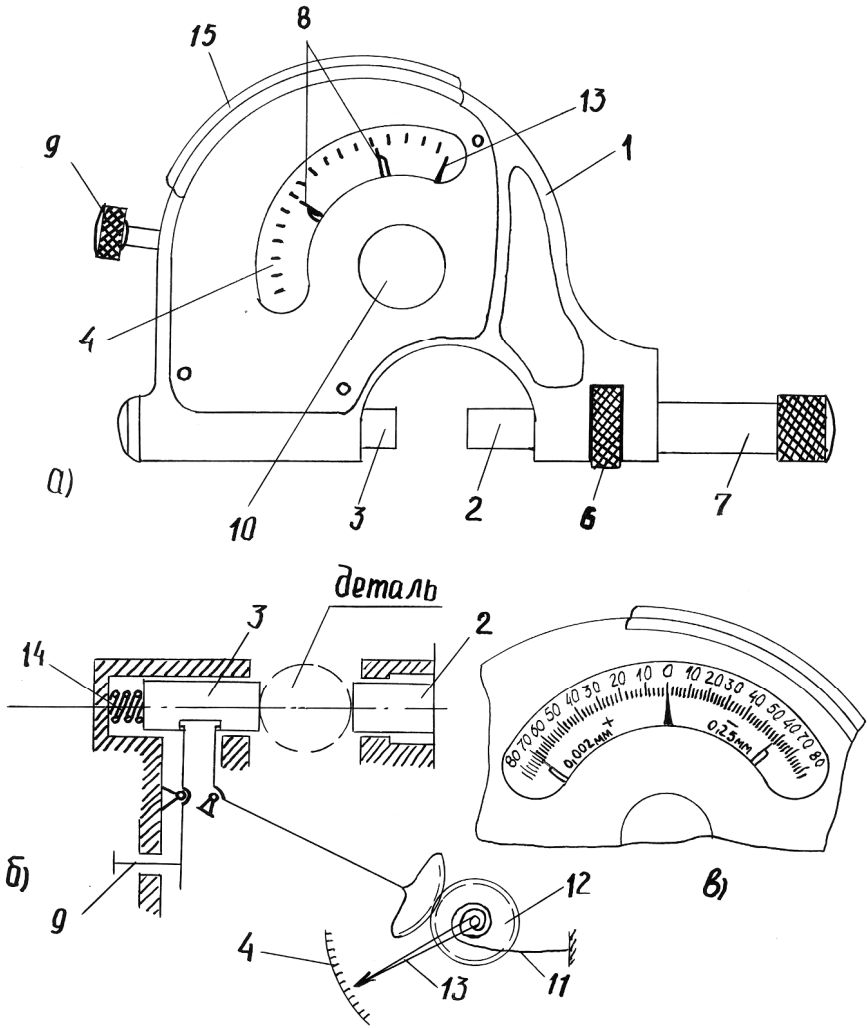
Важільна скоба: *а* – загальний вигляд; *б* – важільно-зубчастий механізм; *в* – шкала; 1 – корпус; 2 – переставна п'ятка; 3 – рухома п'ятка; 4 – шкала; 5 – накладка; 6 – гайка; 7 – ковпачок; 8 – покажчики поля допуску; 9 – відводка; 10 – ковпачок з різьбою; 11 – волосина; 12 – шестерня; 13 – стрілка; 14 – пружина
